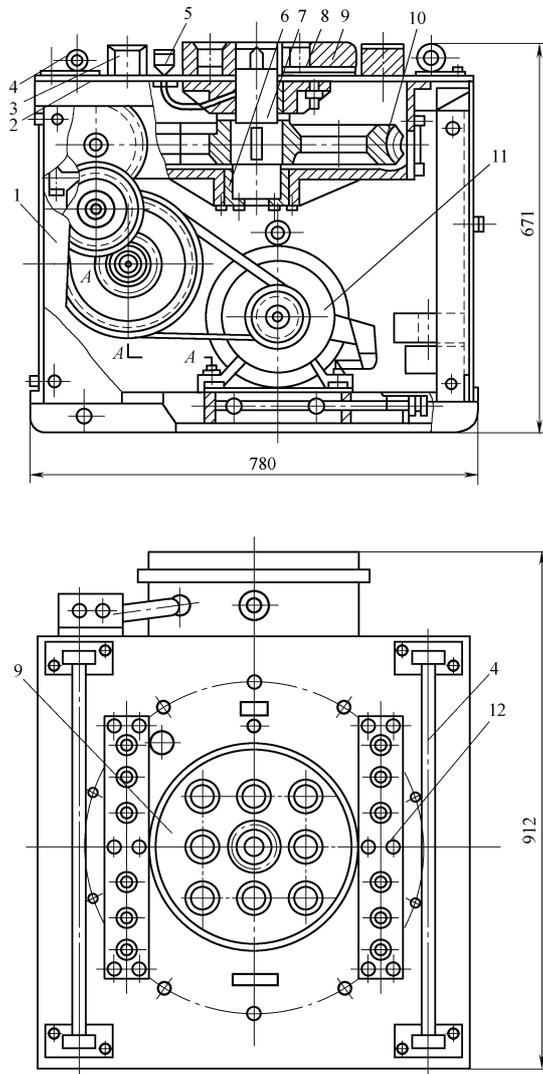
蜗轮蜗杆式钢筋弯曲机构造示意图
